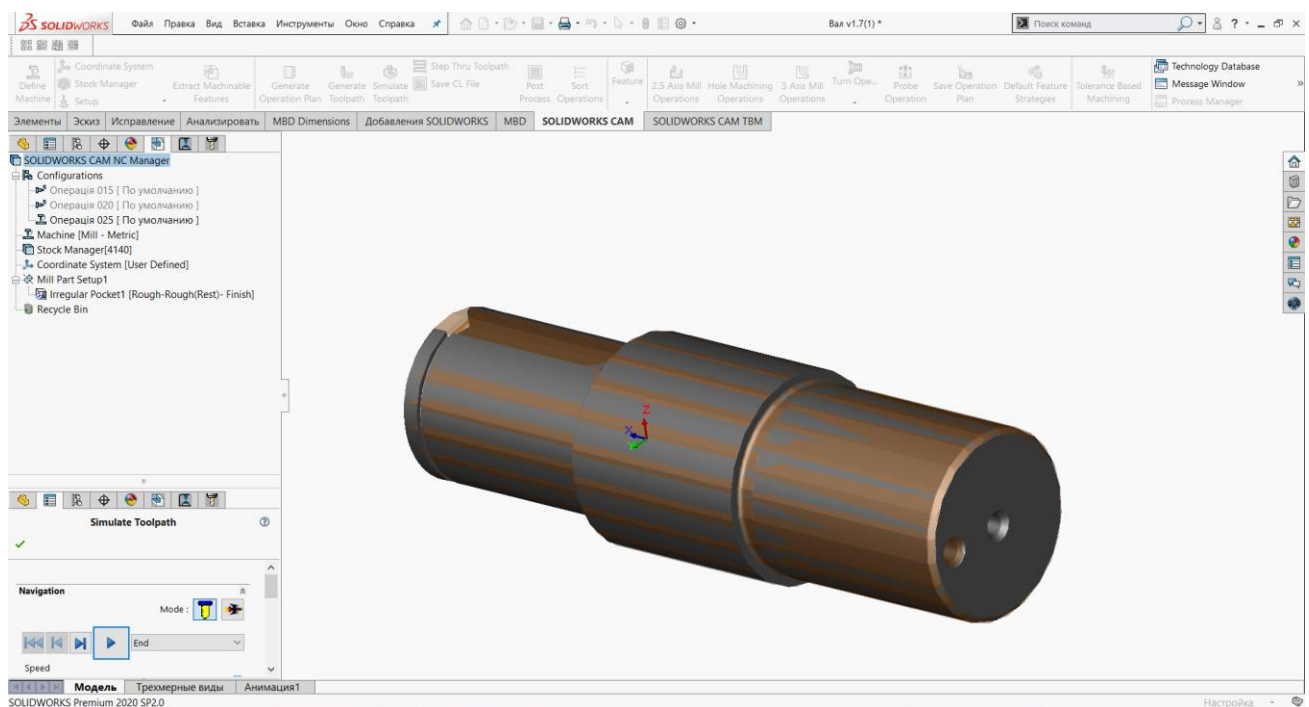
Встановлення деталі у вертикально-фрезерний верстат, для фрезерування шпоночного пазу (установ 3).
